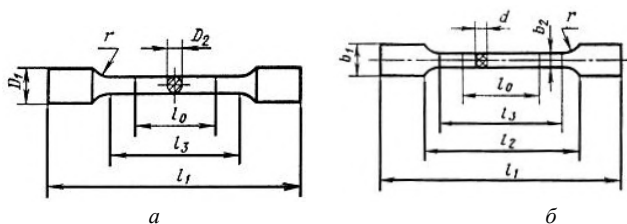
Основные размеры образцов тип 4 (а) и тип 5 (б)
